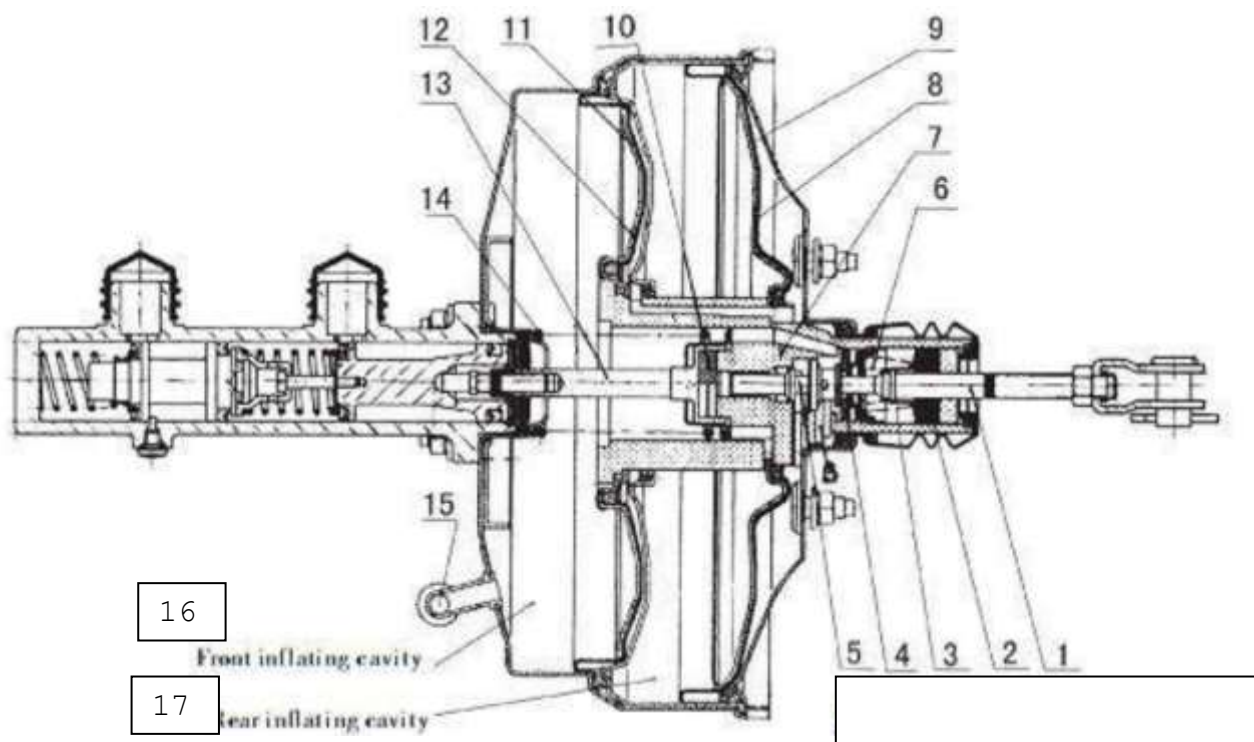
Конструкция вакуумного усилителя и главного тормозного цилиндра:
